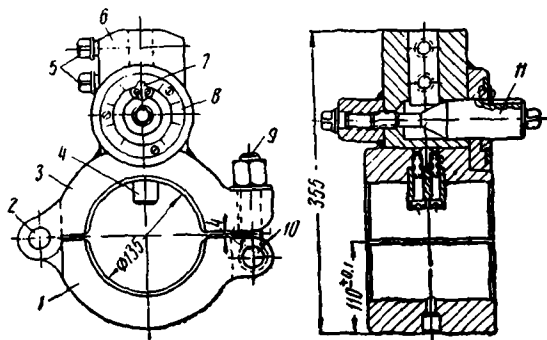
Приспособление для расточки горловин остова под посадку подшипниковых щитов:
